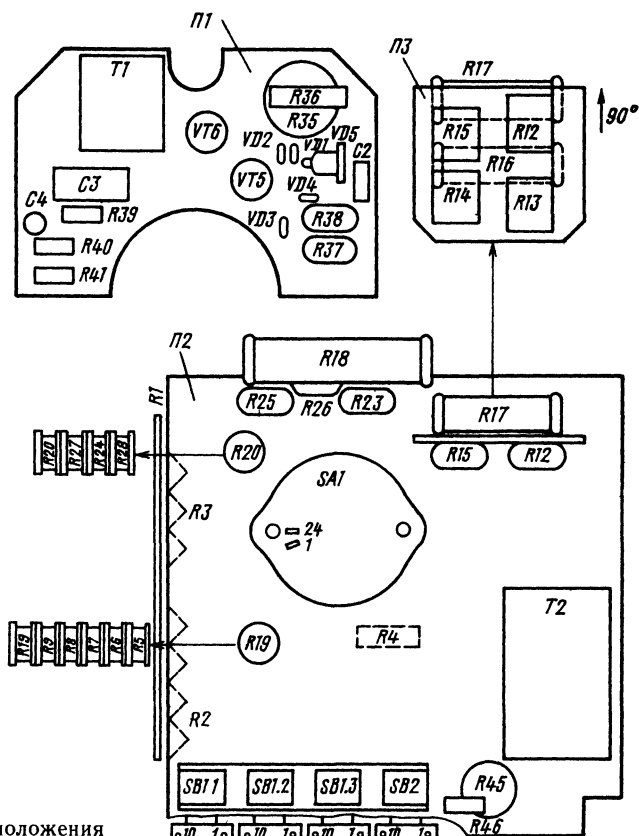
Схема расположения элементов на платах П1—П3, резисторных сборках и расположении секций и контактов переключателя SB1 прибора Ц4340
